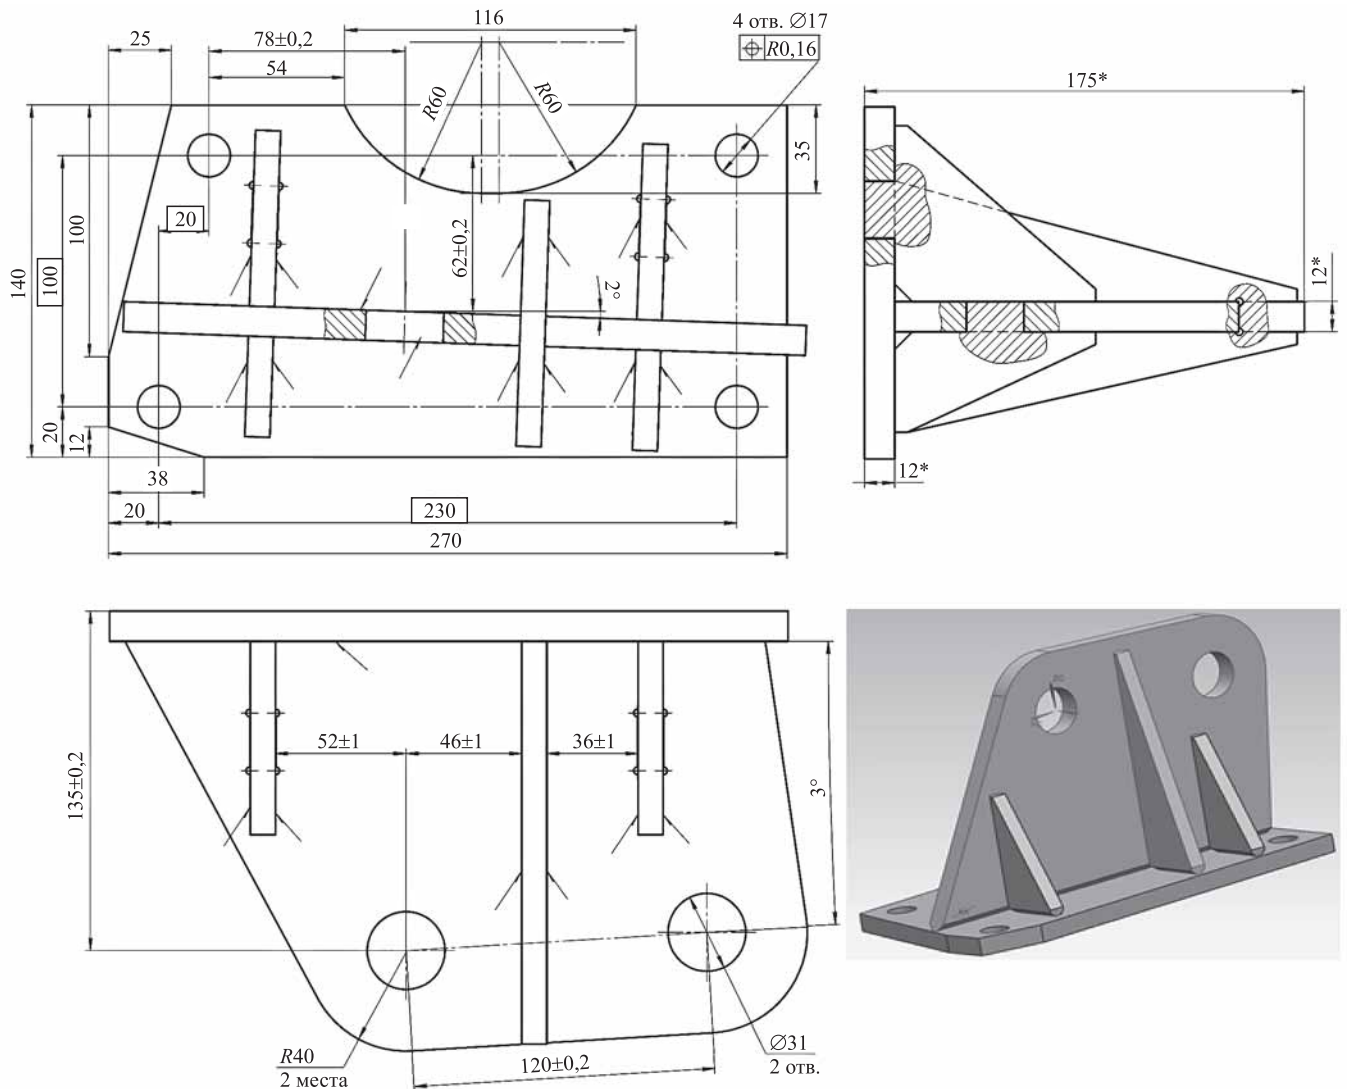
Конструкторский чертеж и общий вид детали "кронштейн подвески раздаточной коробки"
